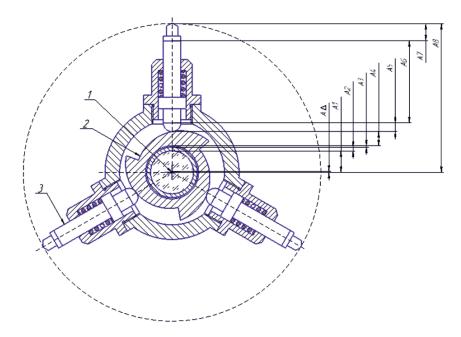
Схема типового центроискателя и размерная цепь его опоры
